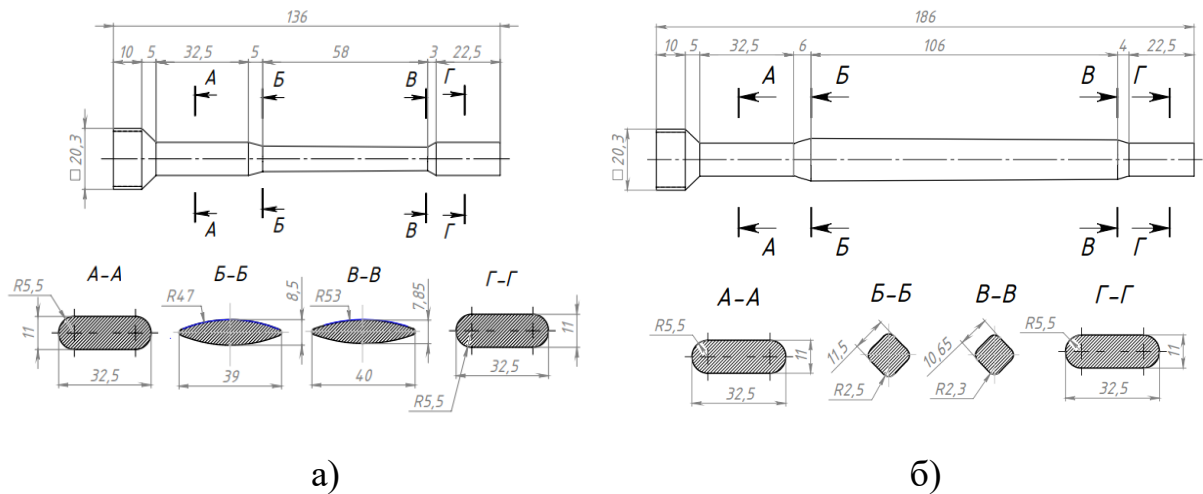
Форма и размеры заготовки после горячей вальцовки в ручьях переменного сечения: а – первый переход; б – второй переход
